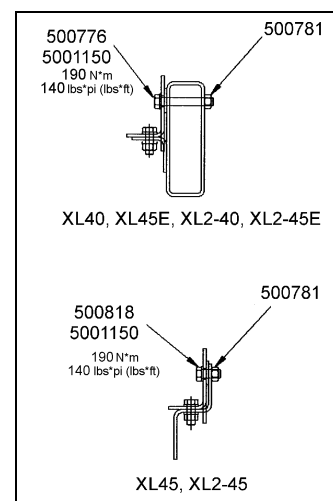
BOULONS DE FIXATION HORIZONTAUX
